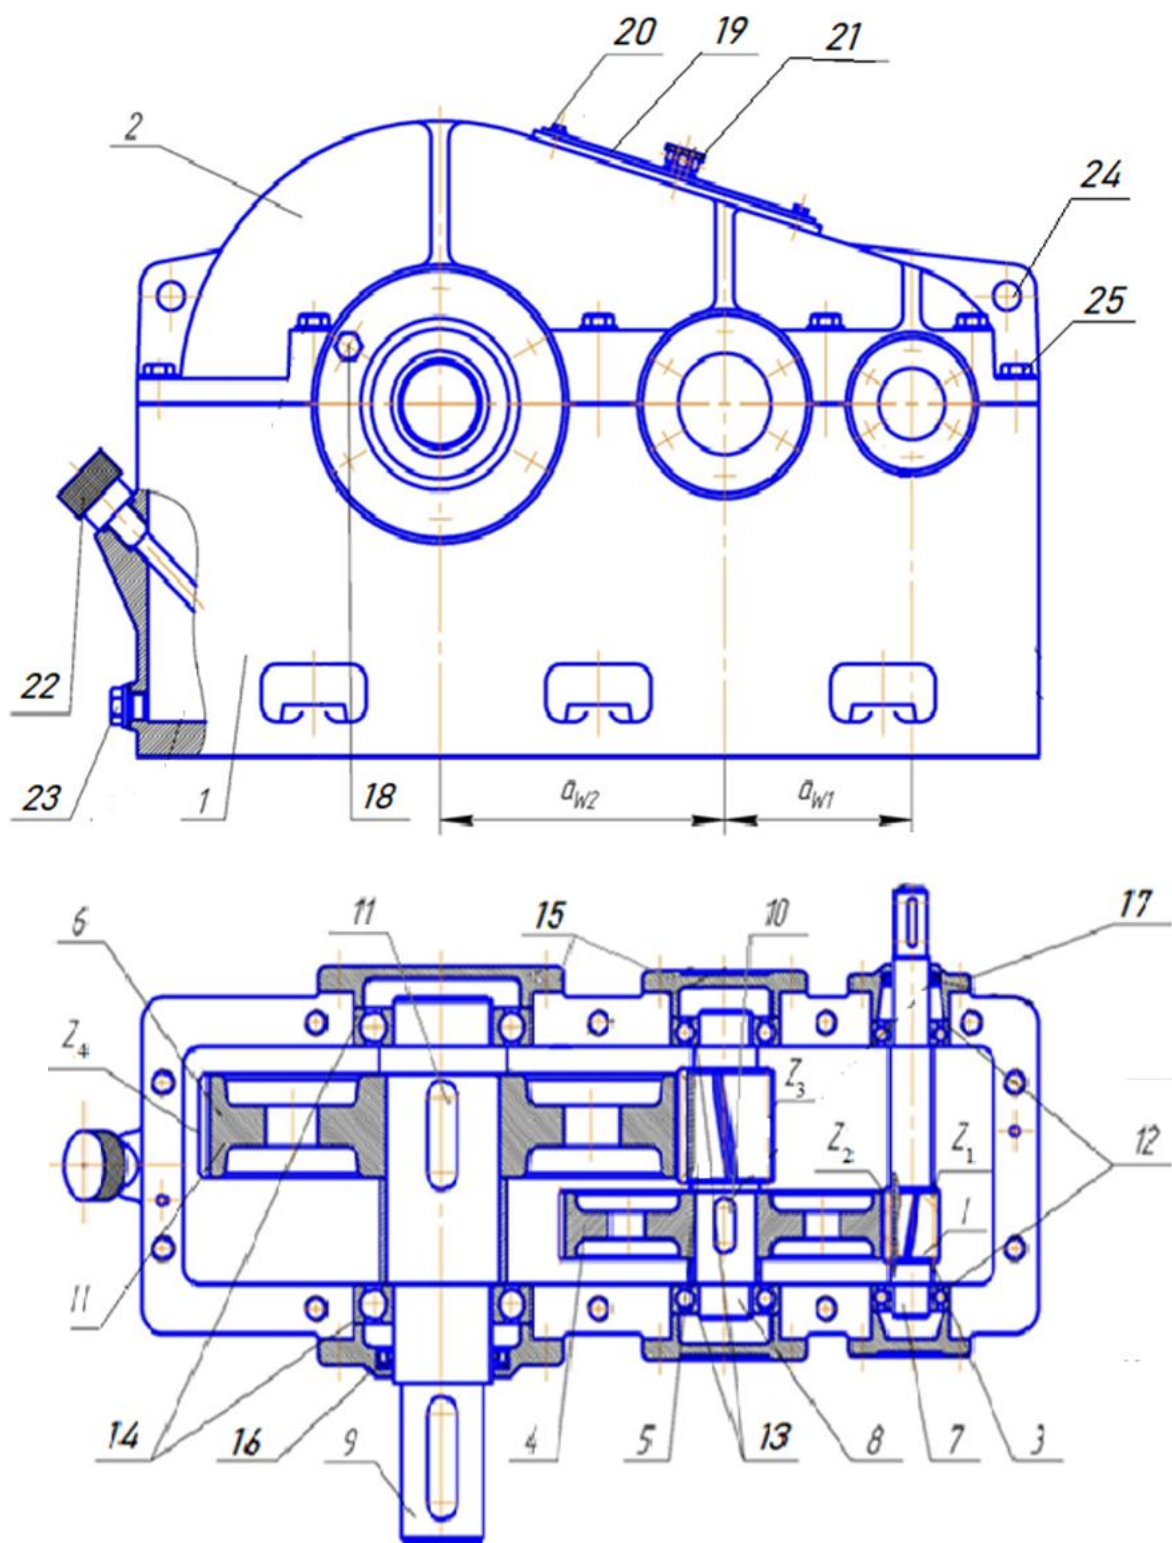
Цилиндрический зубчатый двухступенчатый редуктор
